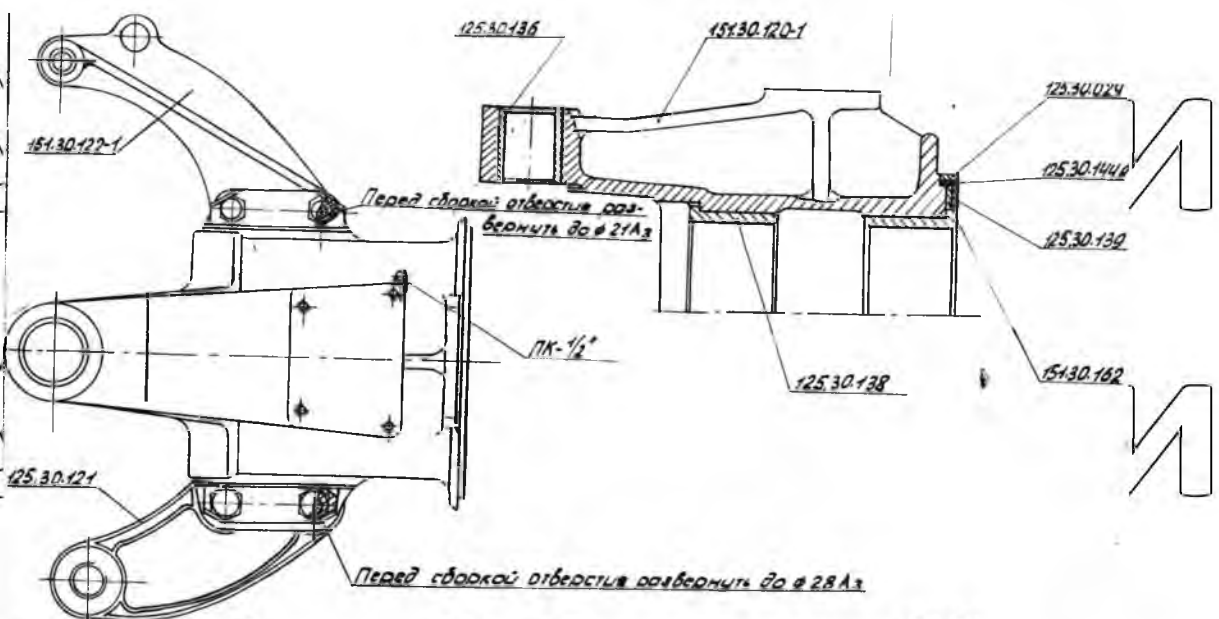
Корпус шарніра в зборі 171.30.018А
